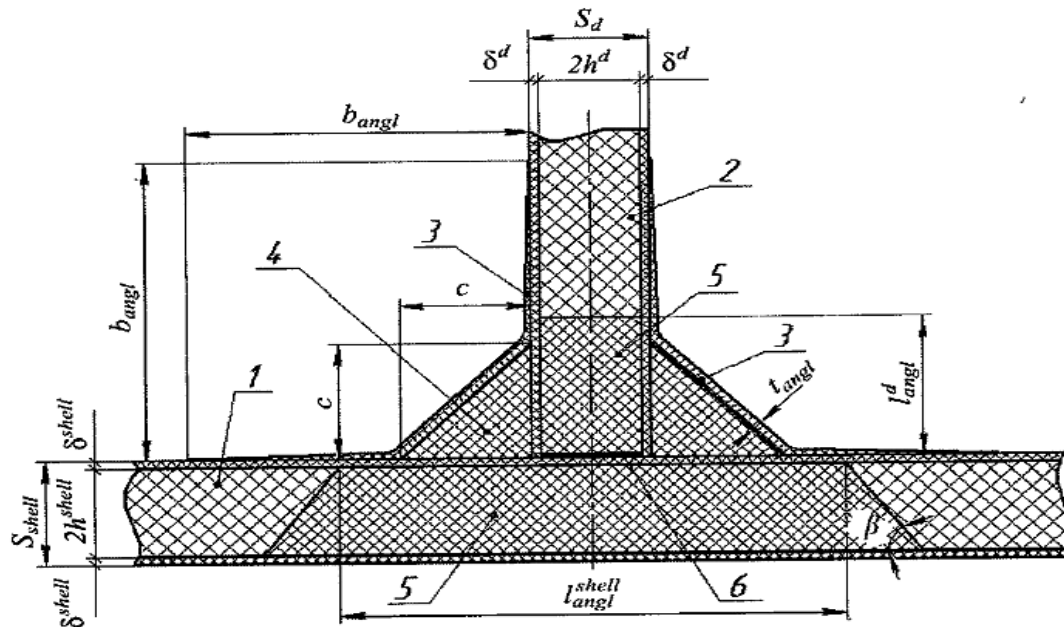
Конструктивна схема кутового формованого з'єднання:
